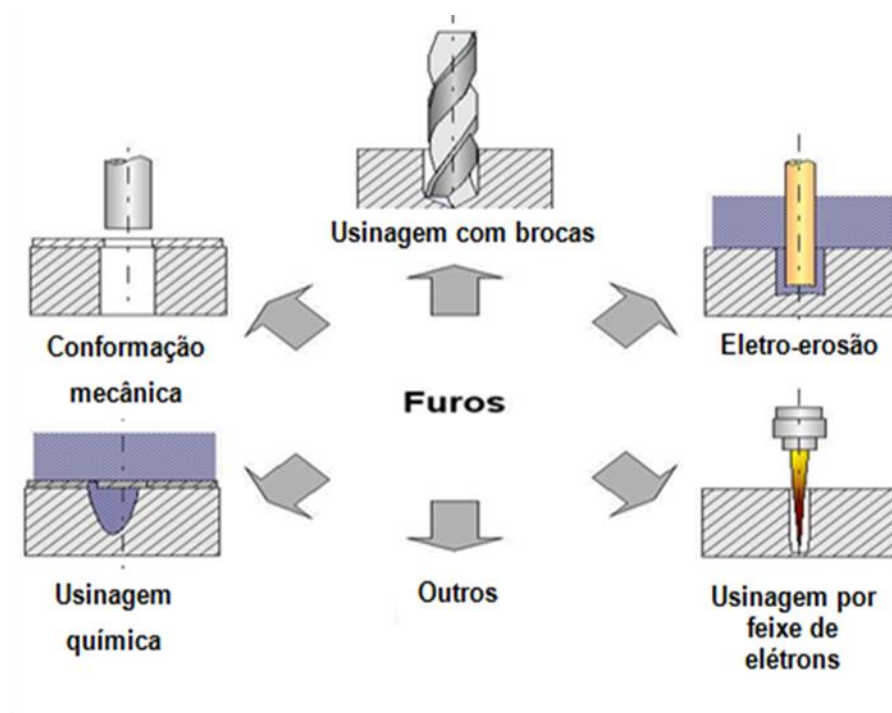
Processos de usinagem para fabricação de furos (Adaptado de Stoeterau, 2008).
